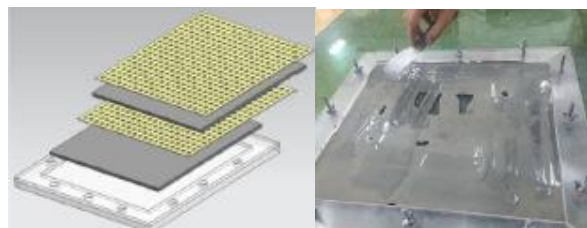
Esquema de moldagem (a) e procedimento inicial de moldagem (b). Fonte: Autor
